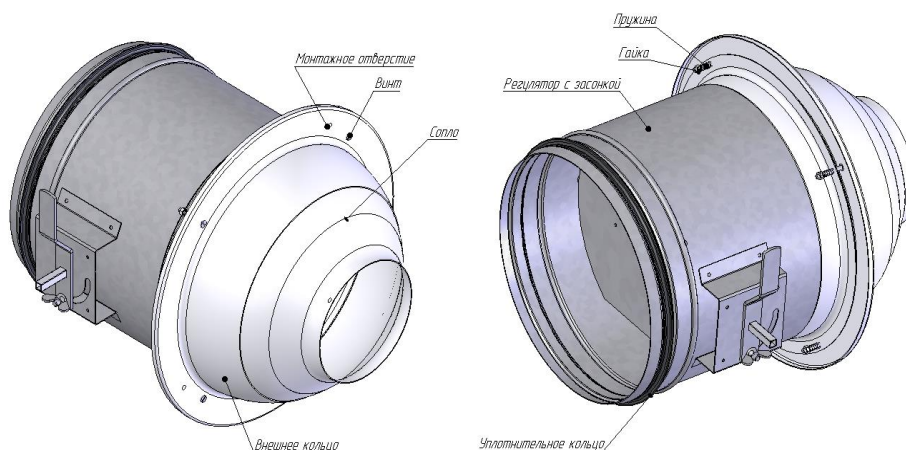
Внешний вид и конструктивные элементы ЗСДКР.
